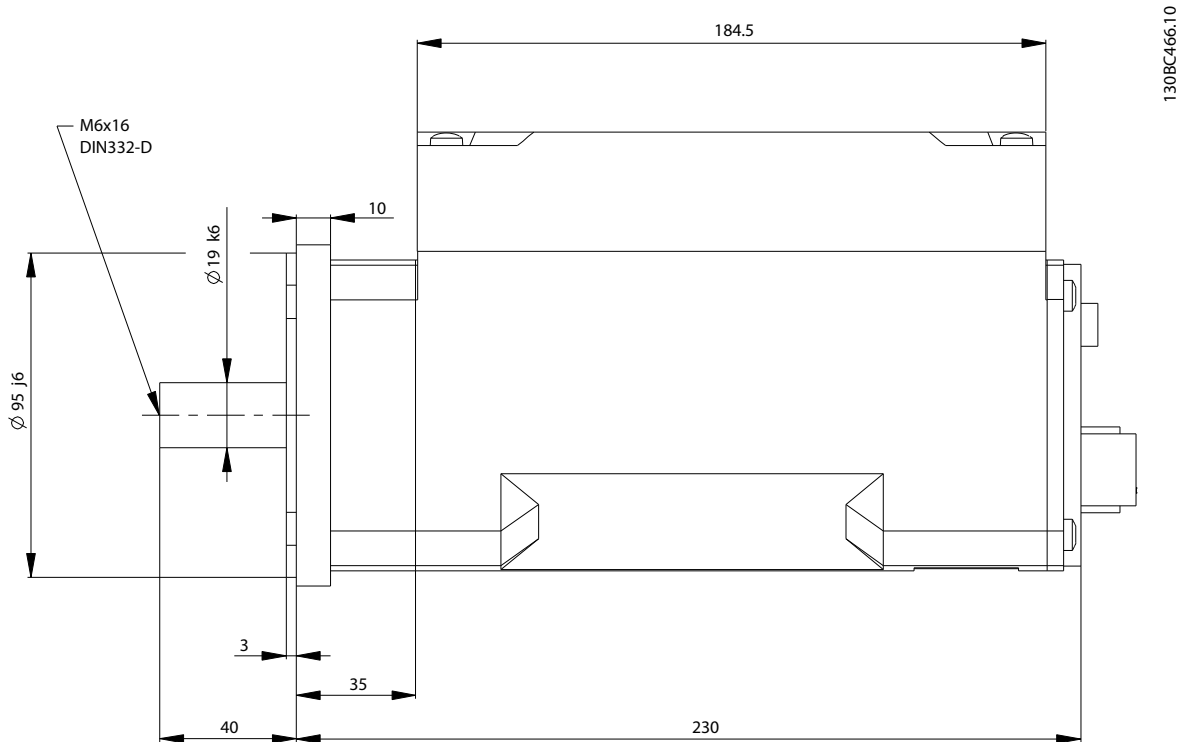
Seitenansicht: Servomotor mit ISD Flansch, ohne Bremse
